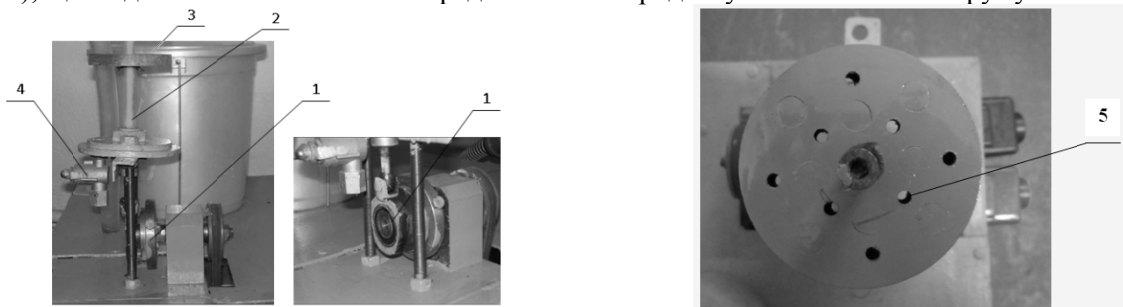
Конструкція робочого органу та приводу гомогенізатора: 1 – кривошипний механізм; 2 – шток; 3 – поршень; 4 – випускний вентиль; 5 – циліндричні отвори в поршні
